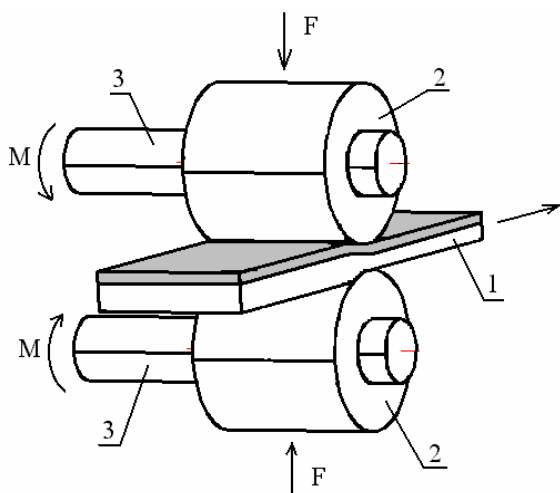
Схема испытания материала с покрытием на обжим в цилиндрических роликах: 1 – заготовка с покрытием; 2 – цилиндрические ролики; 3 – приводные валы, F – сила сжатия валков, M – крутящий момент
